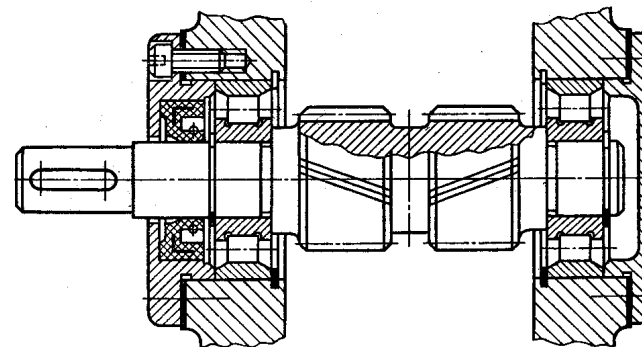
Плавающий вал-шестерня (шевронного редуктора)
